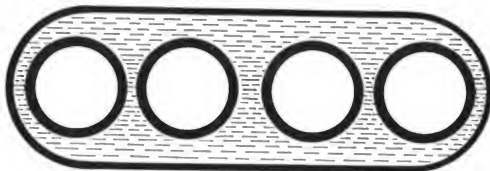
Zylinderblock mit 4 vollständig vom Wasser umspülten Zylindern.
